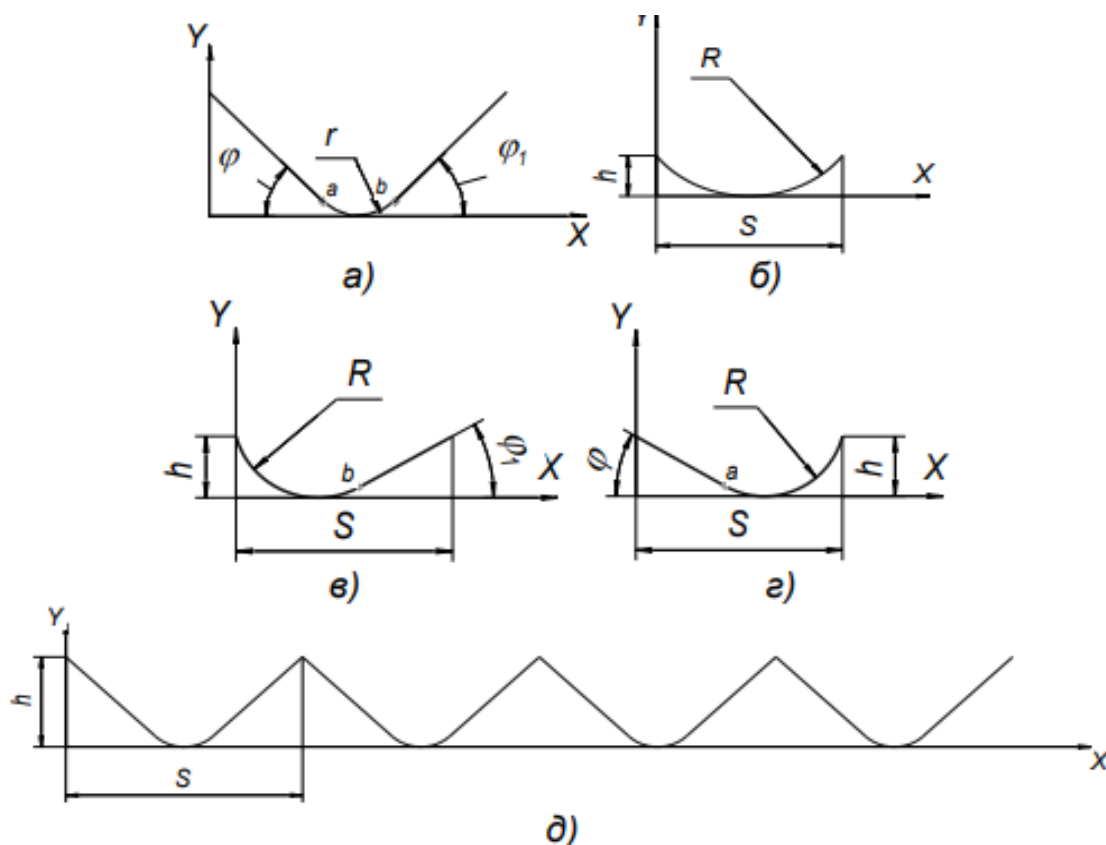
Розрахунок профілю обробленої поверхні копіюванням профілю інструменту:
